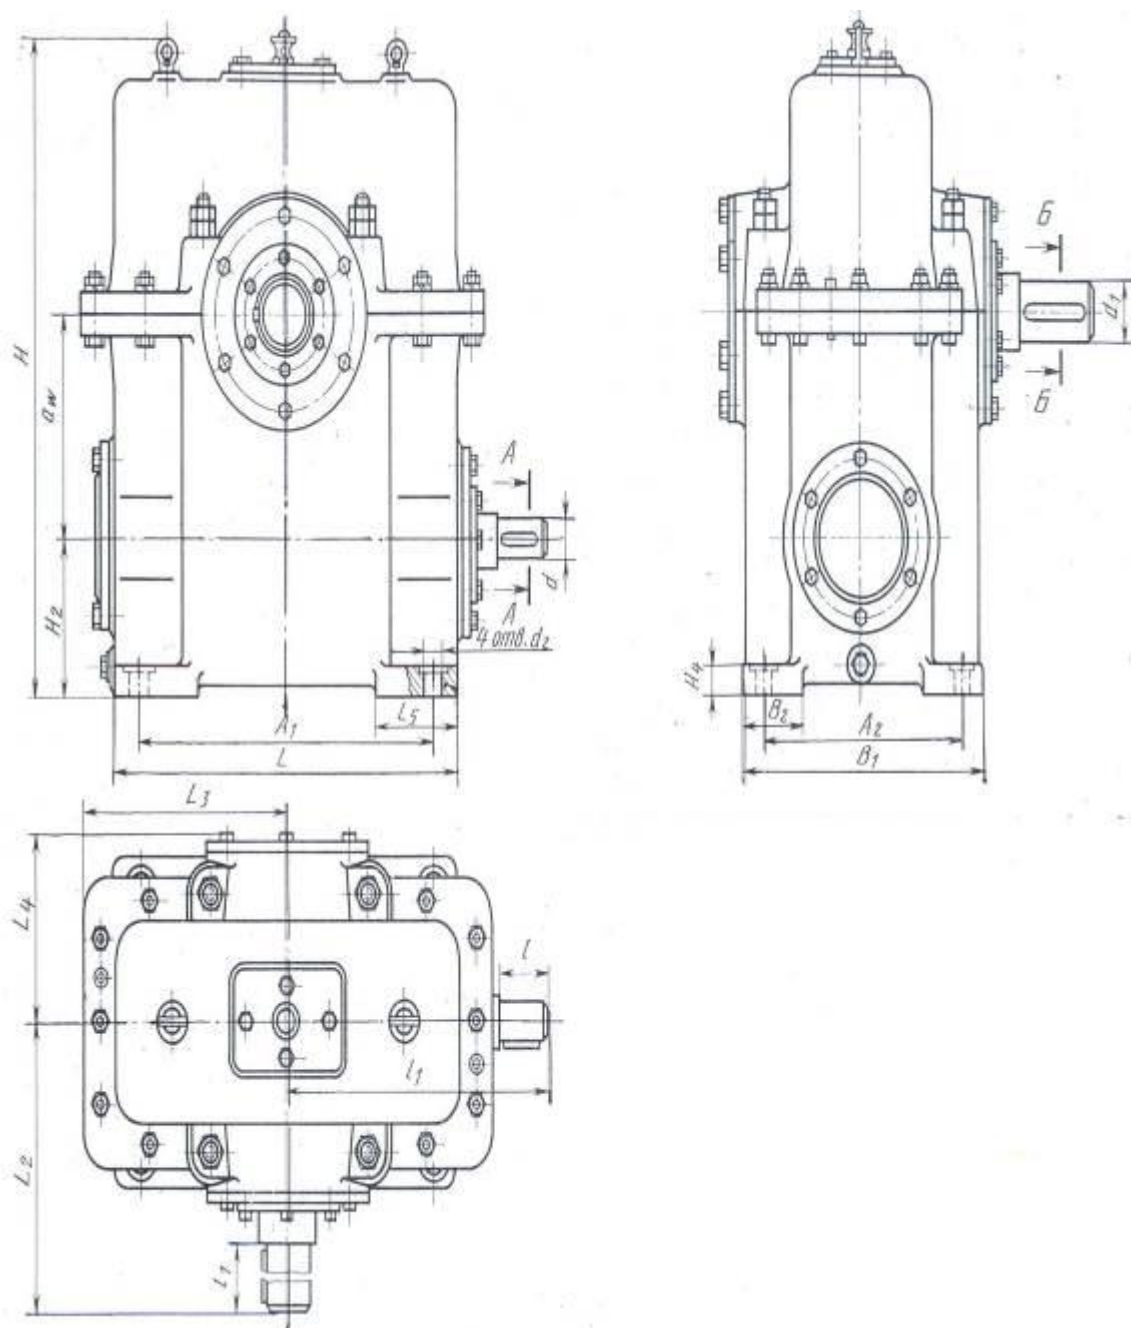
Габаритные и присоединительные размеры червячного редуктора
